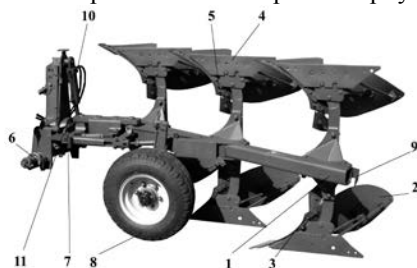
Конструкция навесного оборотного плуга ПНО-3-40/55
